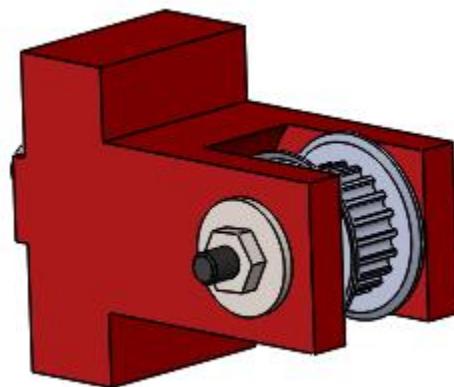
Ensamblaje soporte polea eje y; Fuente: Elaboración propia con SW
